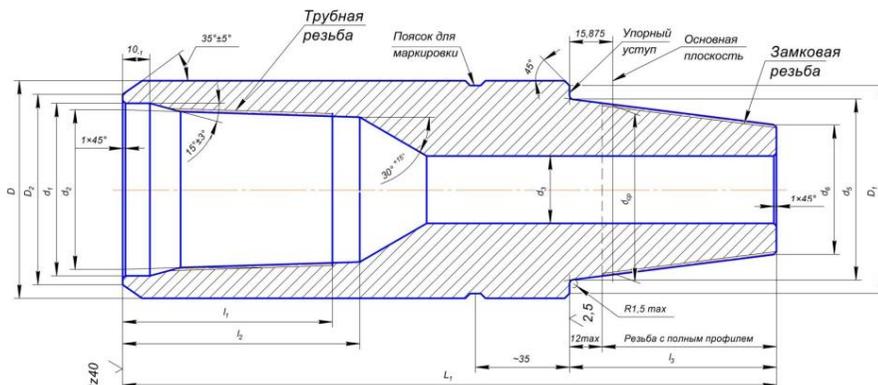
Чертёж ниппеля замков типов ЗН, ЗШ и ЗУ
